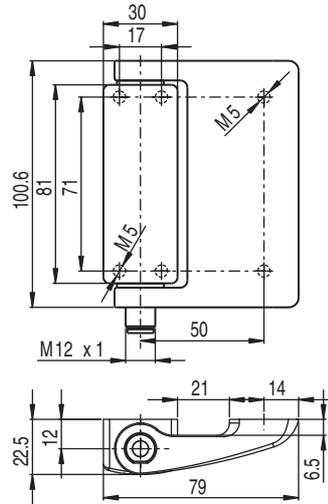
Dimensões do S410-M1M12-B em mm
